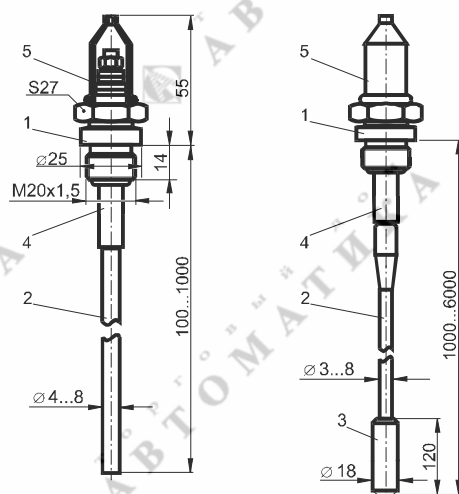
Датчики одноэлектродные, внешний вид и габаритные размеры
